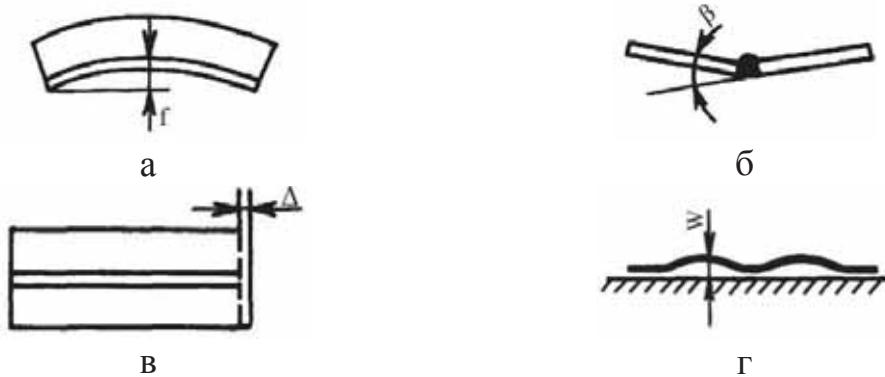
Виды перемещений при деформации сварных конструкций:
